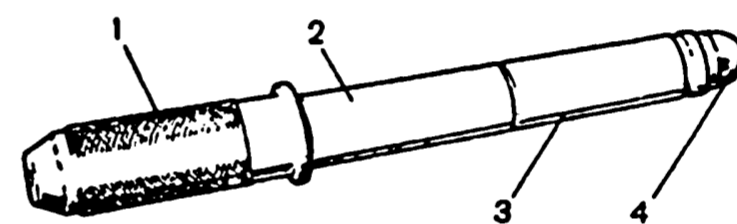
Установка поршневого пальца на приспособление 02.7853.9500 для запрессовки его в поршень и головку шатуна: 1 - валик приспособления; 2 - поршневой палец; 3 - направляющая; 4 - упорный винт
